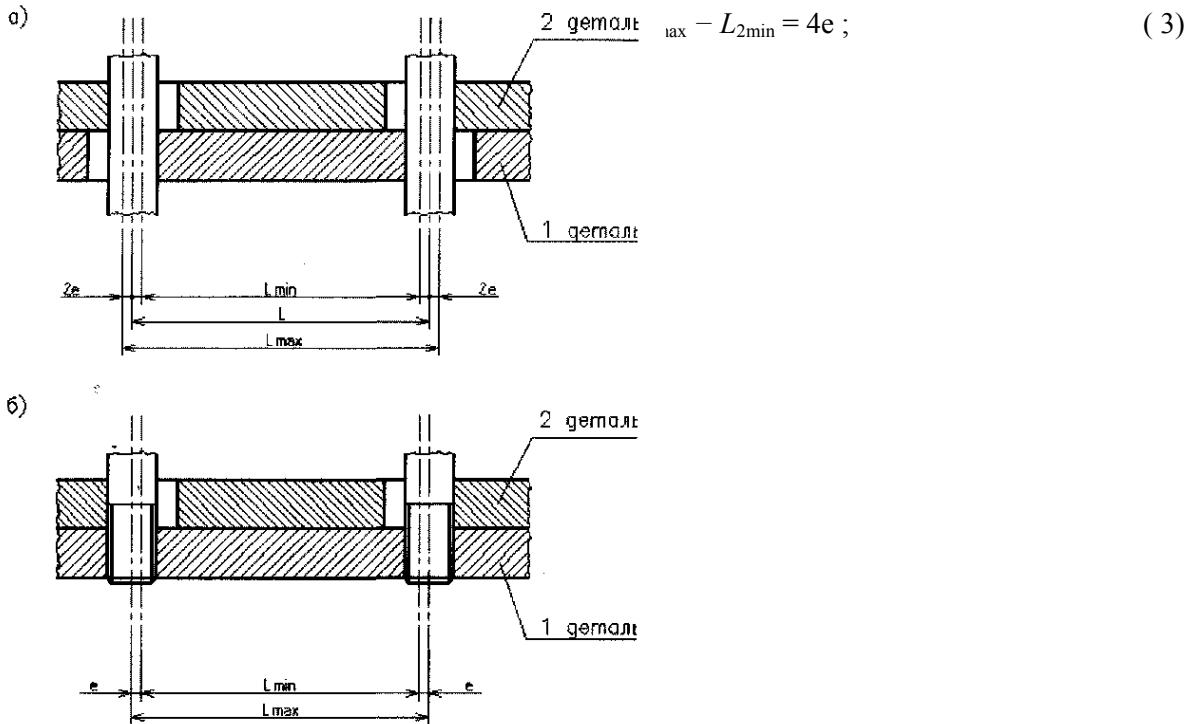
Схемы соединения деталей: а) болтами; б) винтами для противоположных предельных значений
